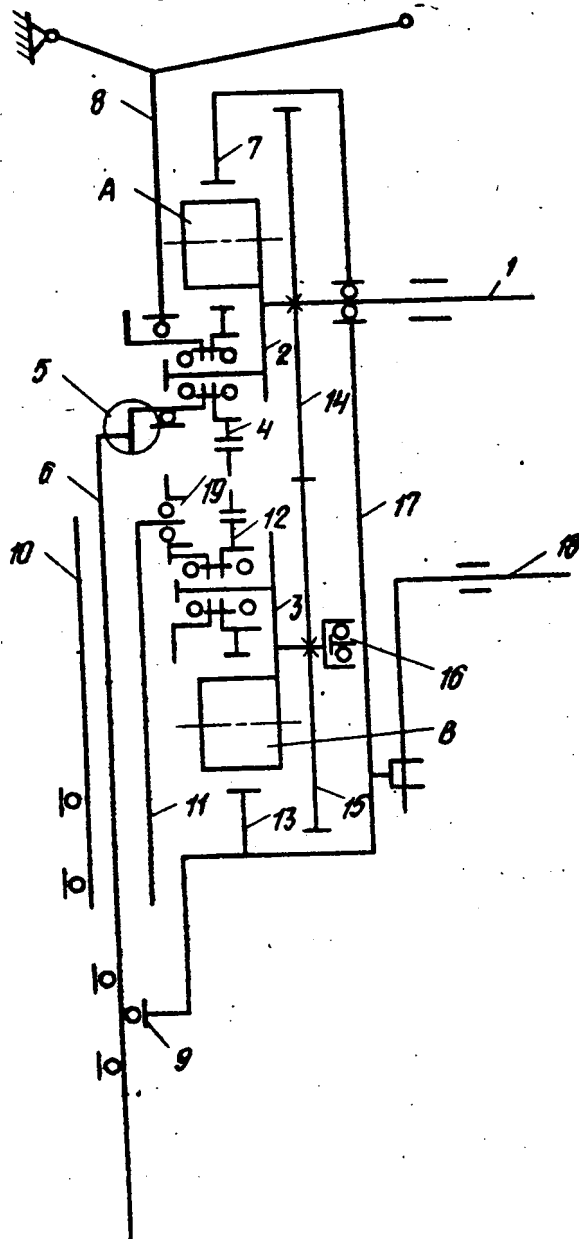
Конструктивна схема механізму голководія швейної машини
